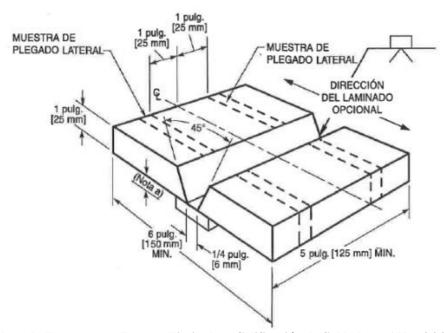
Placa de Ensayo para Espesor Ilimitado — Calificación de Soldadores (Ver 4.24.1) Código D1.1 AWS — 2010
